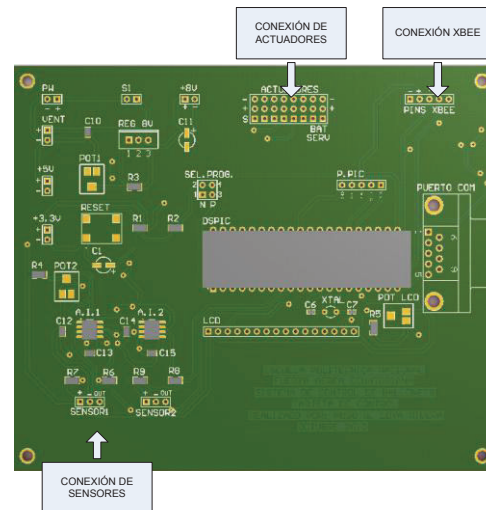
Placa diseñada en ALTIUM DESIGNER.
